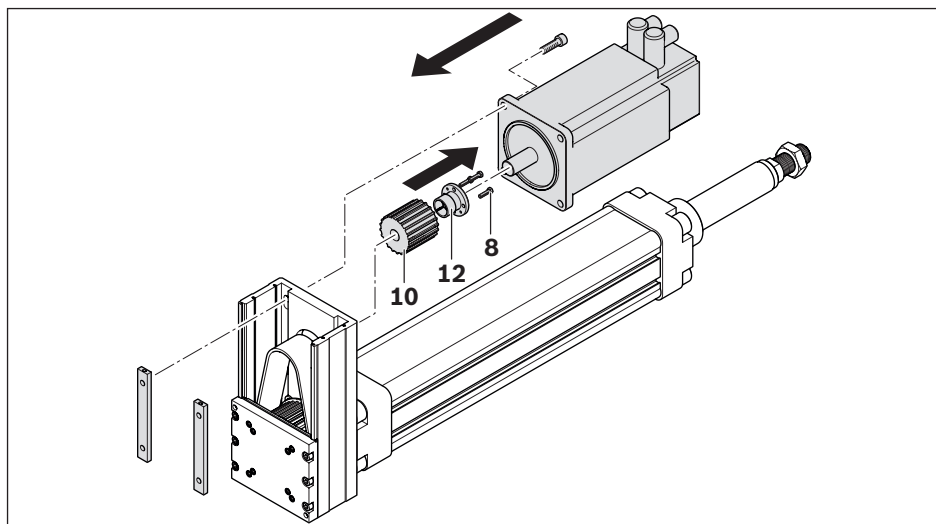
Montaje del motor y de la polea del lado del motor, $i = 2$
